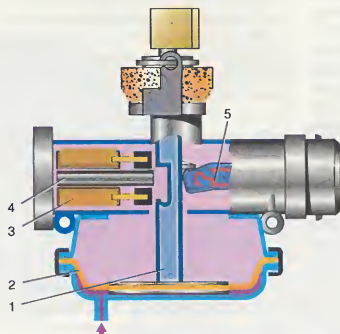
Дверной исполнительный механизм: 1 — штанга; 2 — мембрана; 3 — соленоид; 4 — сердечник соленоида; 5 — контакты.
